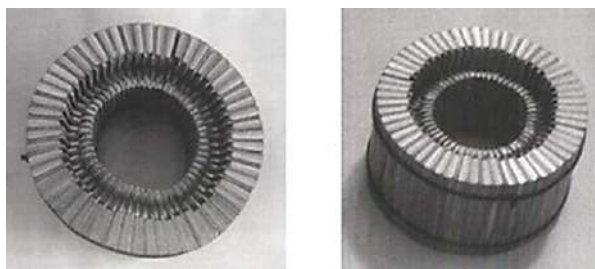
Зібраний пакет колекторного вузла для запресовування
